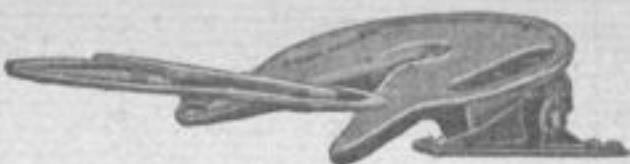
Опорно-сцепное приспособление, на которое опирается передок полуприцепа
